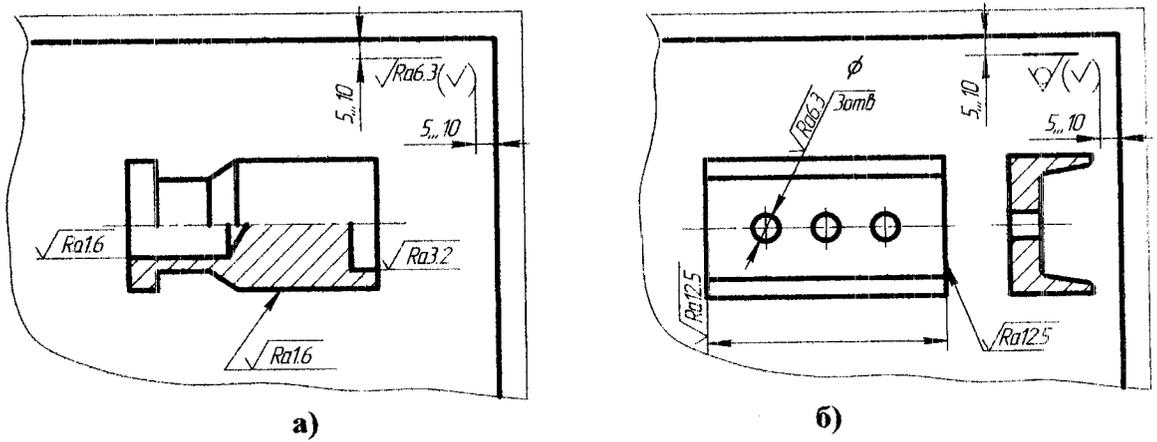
Позначення шорсткості поверхонь деталі, що мають різні значення параметра R_a
